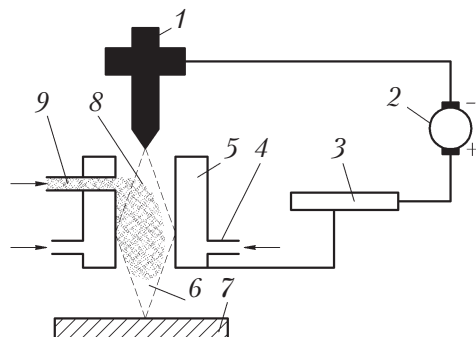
Схема плазменного напыления порошковыми материалами: 1 – электрод; 2 – источник питания; 3 – регулируемое сопротивление; 4 – охлаждающая вода; 5 – плазменная головка (плазмотрон); 6 – плазменный факел; 7 – деталь (заготовка); 8 – дуга; 9 – порошок твердого сплава
